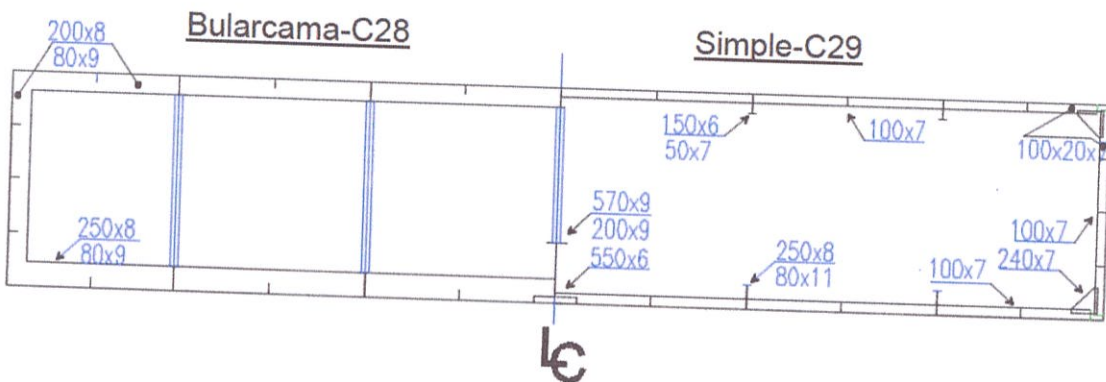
Rayado Estructural de Fondo y Cubierta
